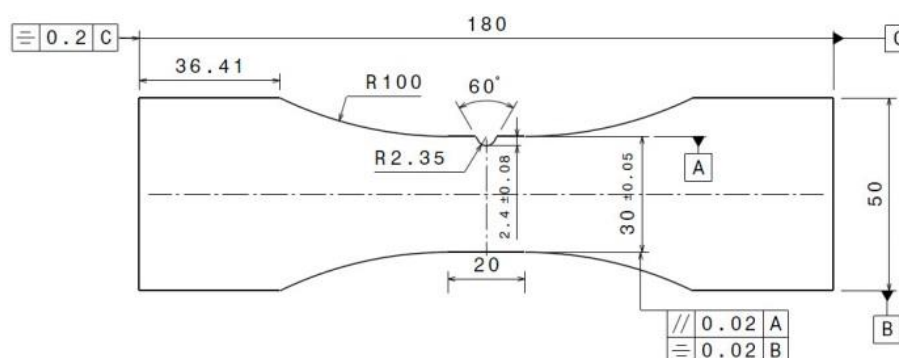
Géométrie de l'éprouvette de fatigue entaillée  $K_t=3$
